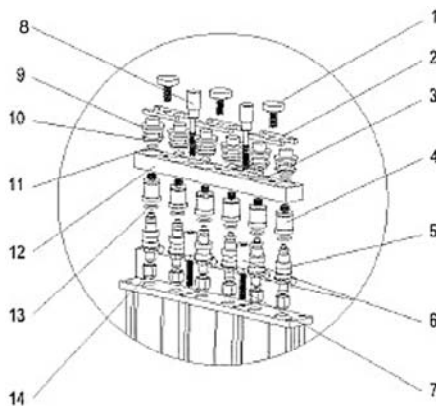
Схема установки топливной рампы для обратной промывки форсунок:
